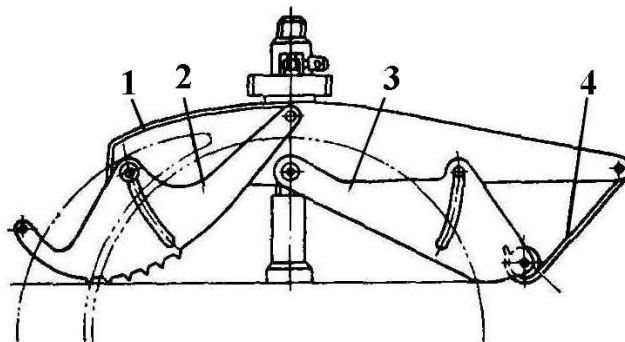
Будова пили кругло пильного верстата для поздовжнього розпилювання, що огорожує:
